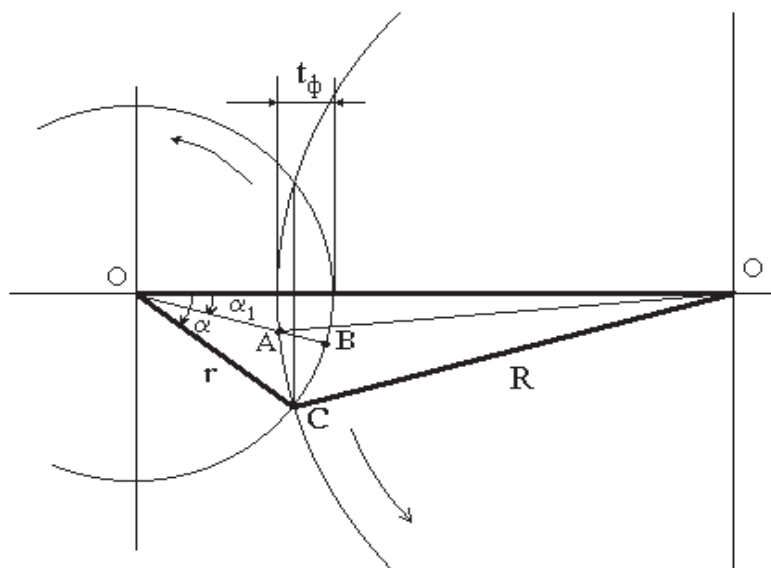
Зона контакта заготовки и круга при врезном шлифовании
